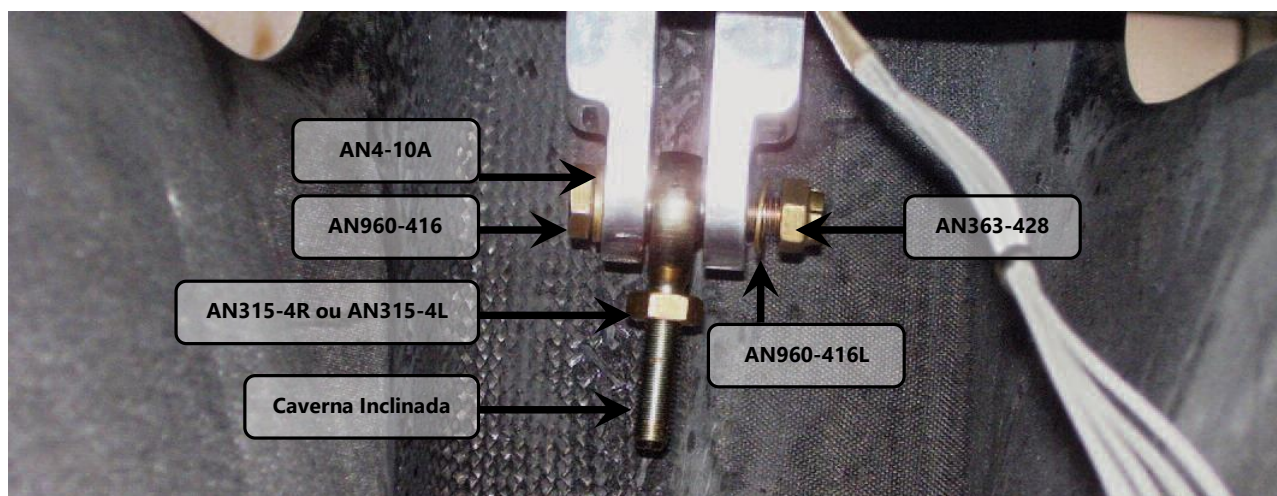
Detalhe de instalação do terminal rotular.
